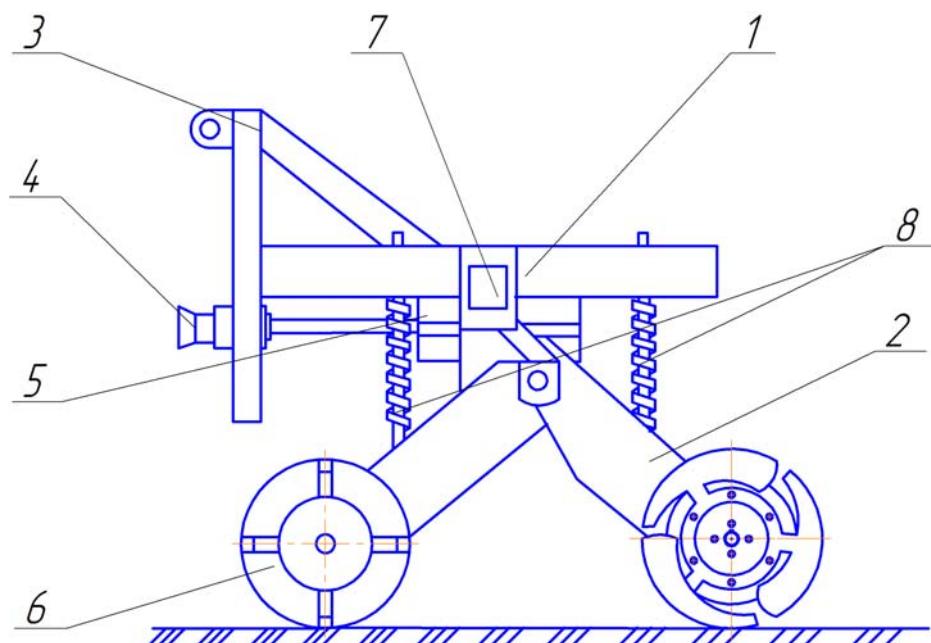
Фрезерний культиватор-гребнеутворювач КГФ-2,8 з удосконаленим гребенеутворювачем
